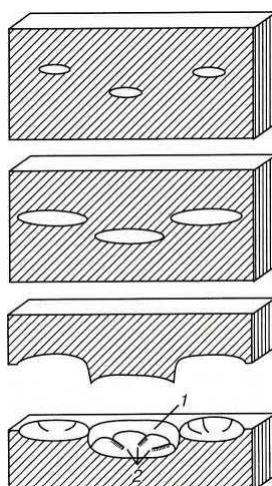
Схема образования квазискола (розеточный излом) [21]: 1 — поверхность сдвига; 2 — отрывные гребни
